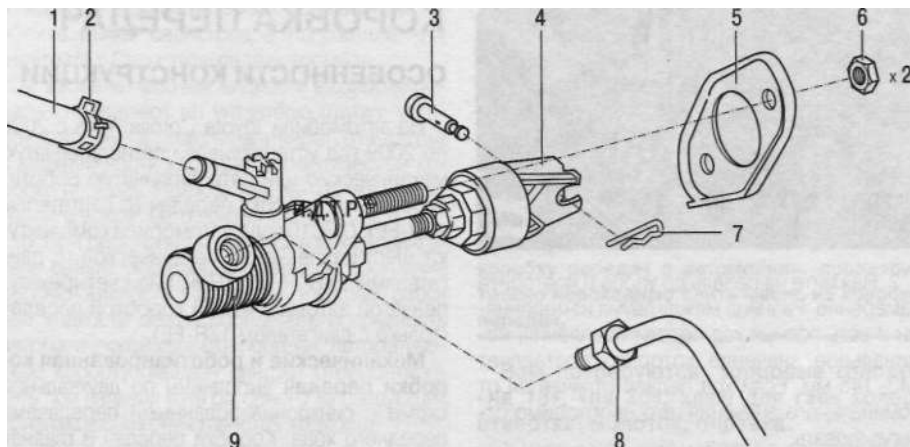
Главный цилиндр сцепления: 1 - патрубок главного цилиндра сцепления; 2 - хомут; 3 - фиксатор; 4 - вилка штока главного цилиндра сцепления; 5 - кронштейн; 6 - гайка; 7 - штифт вилки штока главного цилиндра сцепления; 8 - трубопровод привода сцепления; 9 - главный цилиндр сцепления
